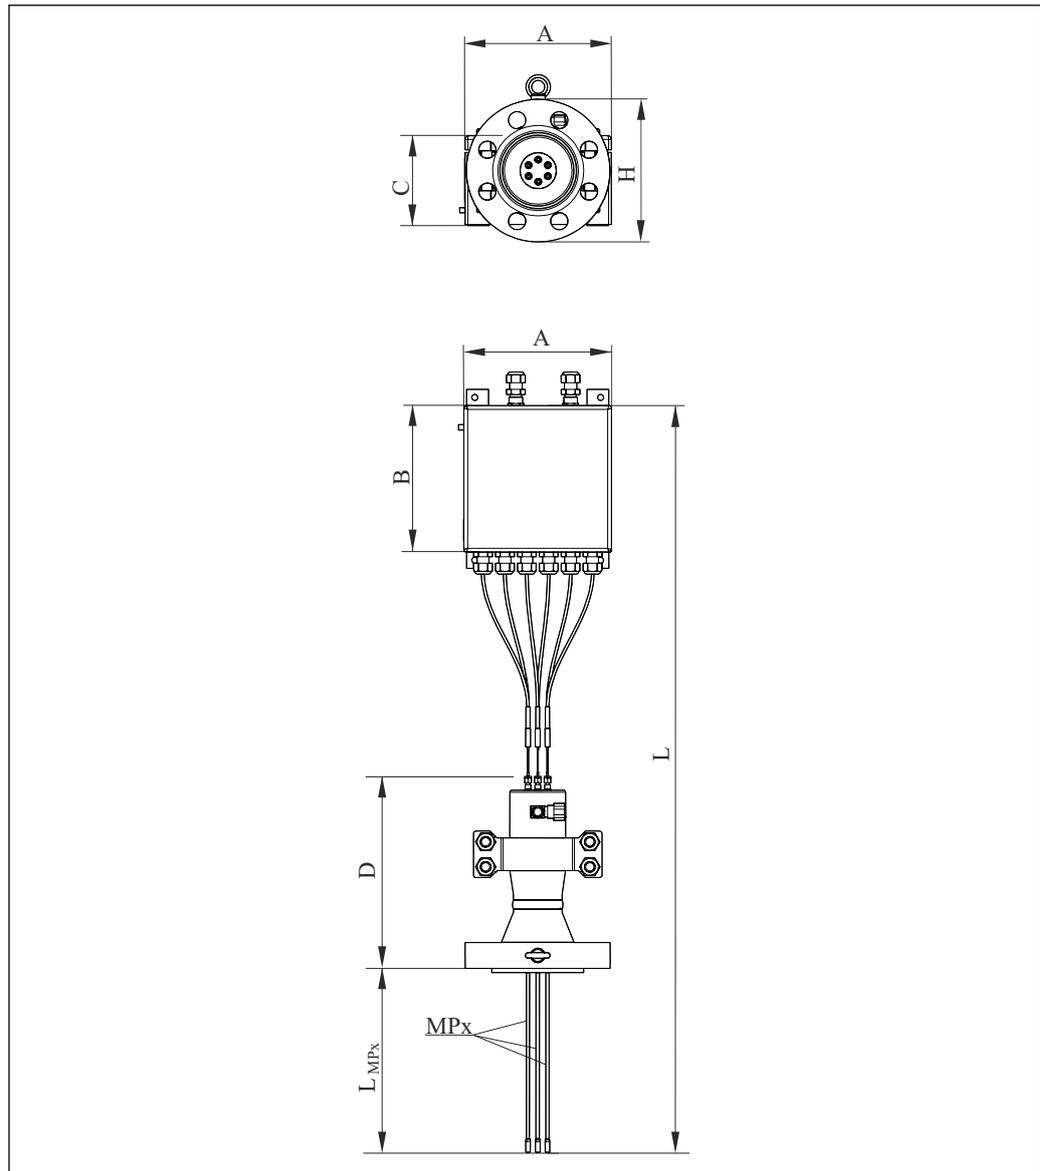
Design del termometro multipunto modulare. Tutte le dimensioni in mm (in)
